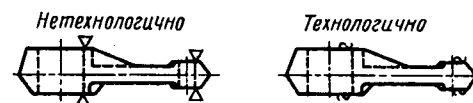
Пример проектирования технологичной конструкции заготовки рычага.
